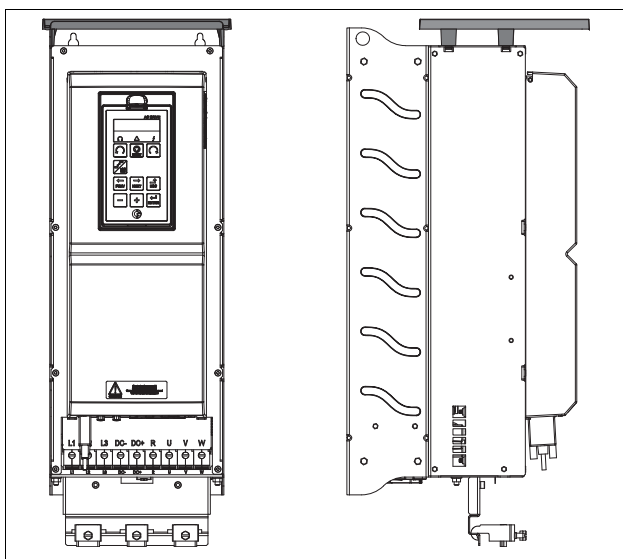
Дополнительная верхняя крышка, установленная на корпусе размера D2
